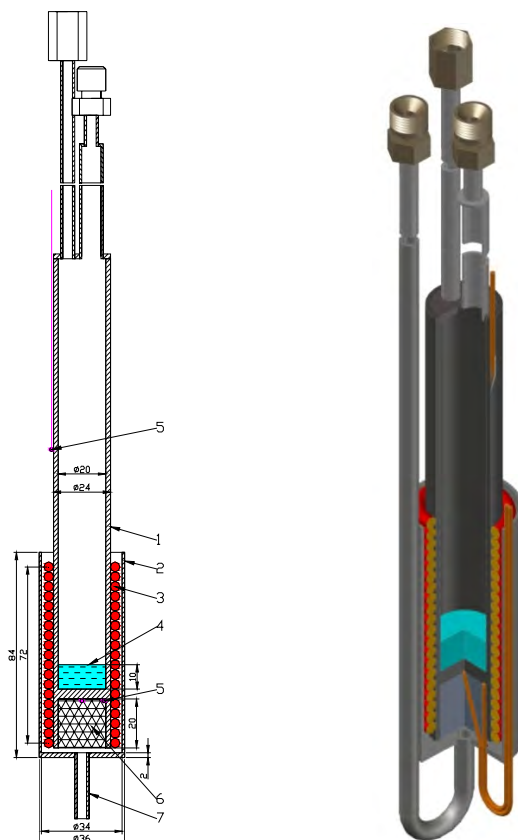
Ампульное устройство: 1 – корпус ампулы (12X18Н10Т); 2 – кожух охлаждения (12X18Н10Т); 3 – нагреватель; 4 – образец; 5 – термопары; 6 – теплоизоляция; 7 – труба подачи азота
